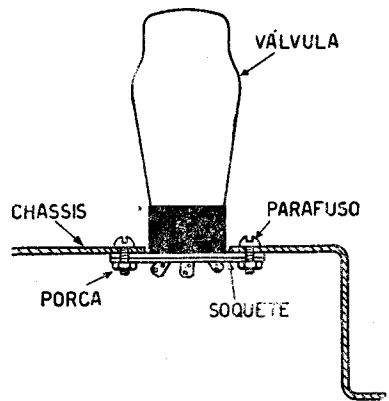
Modo de montar o soquete debaixo do chassi.
